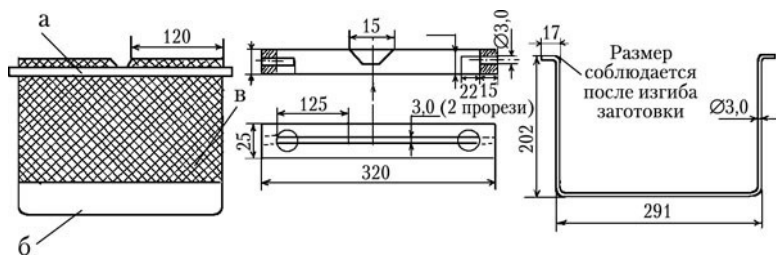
Рамка из черешневой или буковой планки: а – планка рамки; б – проволока; в – вощина
